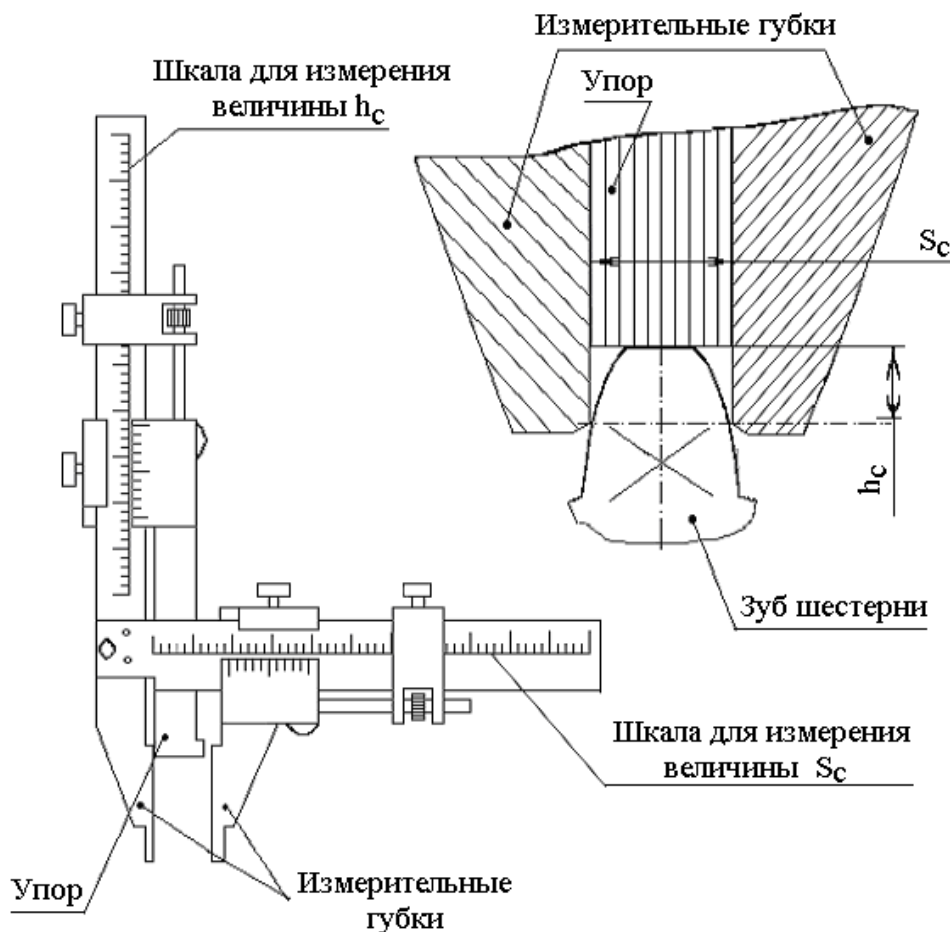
Штангензубомер и схема измерения толщины зуба шестерни
